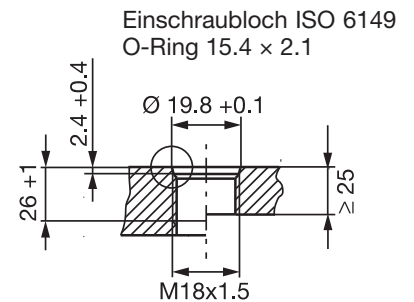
Einschraubloch für die Montage des BTL mit O-Ring
